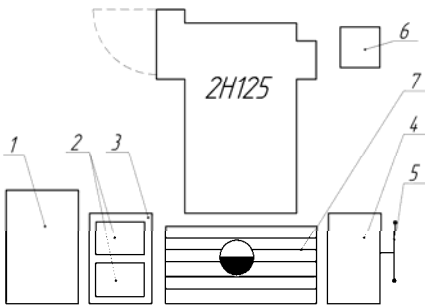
Организация рабочего места сверловщика где: 1 – стеллаж-подставка; 2 – тара; 3 – столик приёмный; 4 – тумбочка инструментальная двухсекционная; 5 – планшет для чертежей; 6 – стеллаж для приспособлений; 7 – решетка под ноги
